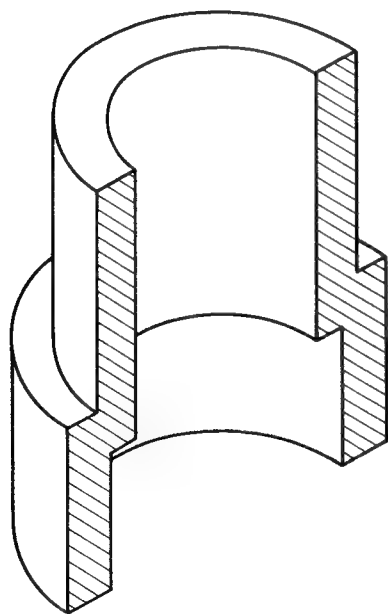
Sección axial de un casquillo cilíndrico.
